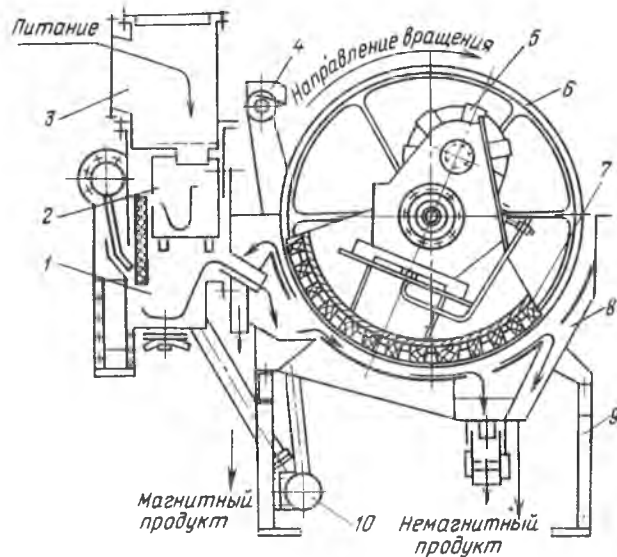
Барабанный магнитный сепаратор ПБМ-150/200:
